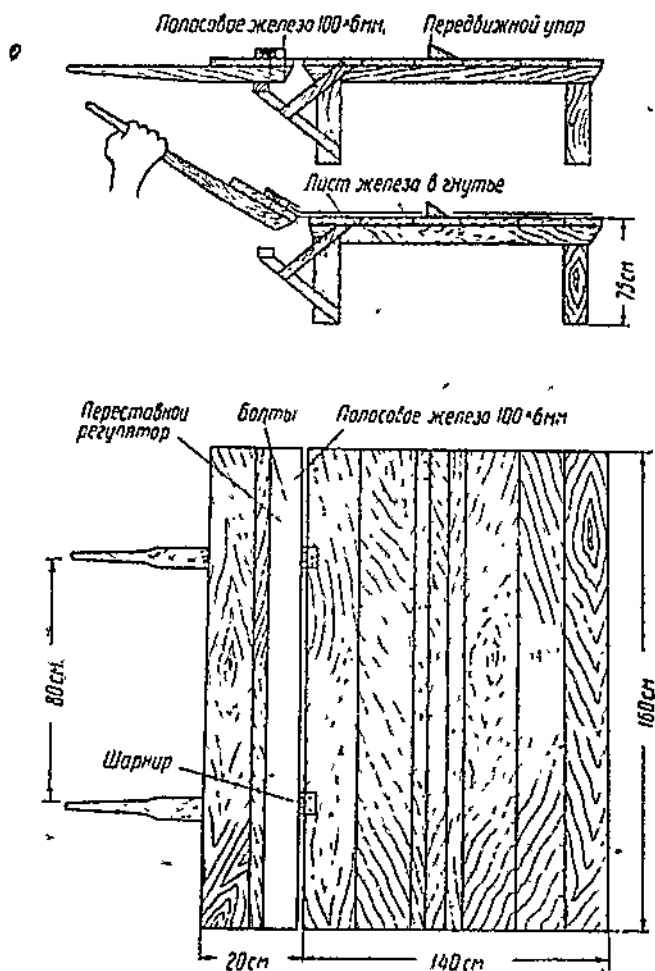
Приспособление Хрянина для загибания кромок листов и изготовления фальца.
